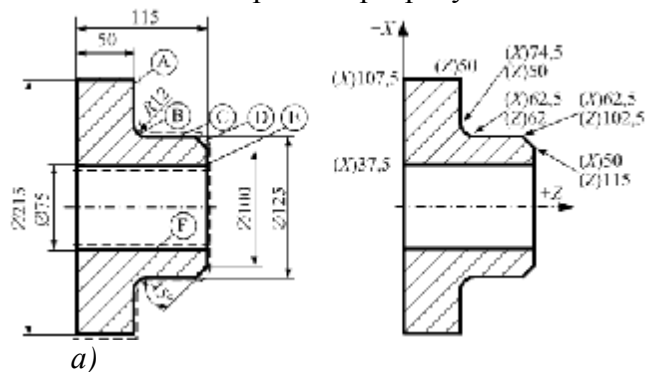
Креслення заготовки (*a*) та її розміри в абсолютних координатах (*б*); штриховою лінією показаний контур заготовки до обробки
